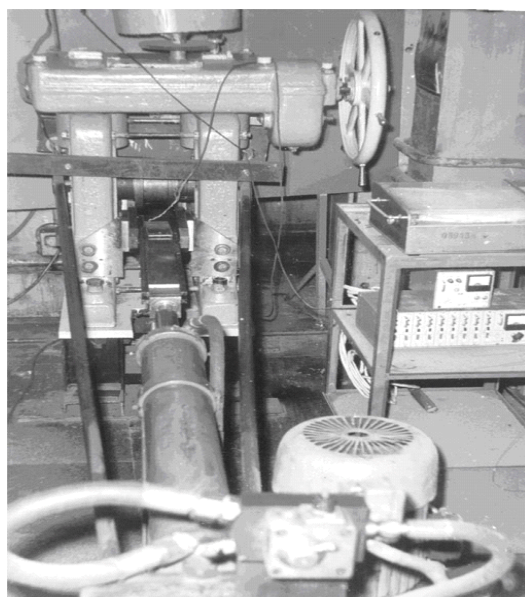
Установка для периодической прокатки полосовых заготовок
